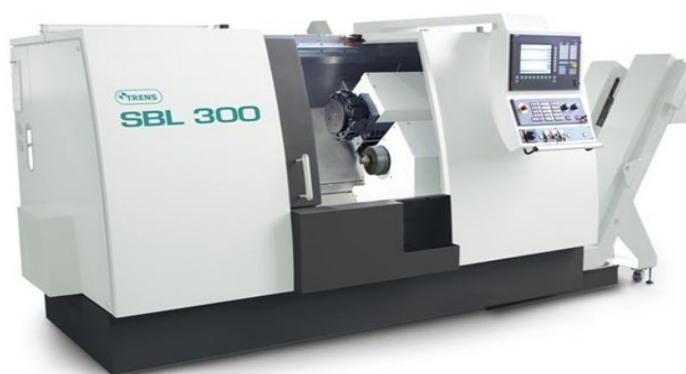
Токарный станок с ЧПУ TRENS SBL 300 CNC
